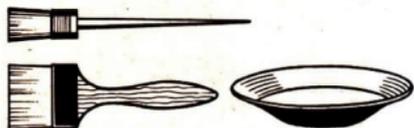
/2 Werkzeuge und Hilfsmittel zum Beizen und Färben
